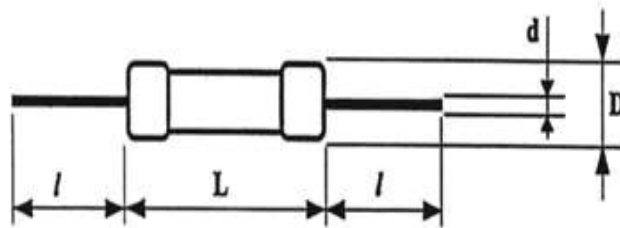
Креслення корпусу резисторів С2-23
